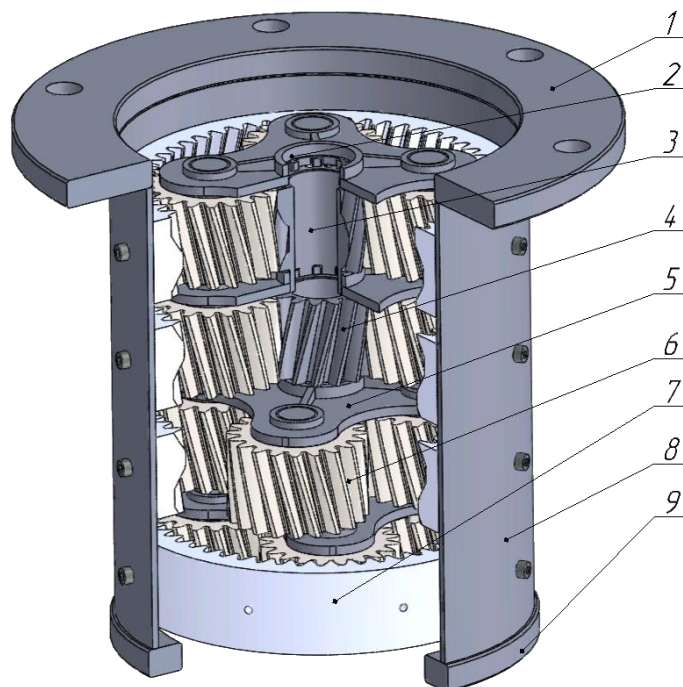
Компьютерная модель сборки планетарного редуктора (поступенчатый разрез): 1 – фланец для крепления к мачте, 2 – пазы зацепления с фланцем спирального диска трехкулачкового блока, 3 – сквозное отверстие, 4 – малая шестерня (солнце), 5 – водило, 6 – большая шестерня-планета (сателлит), 7 – эпицикл, 8 – корпус редуктора, 9 – фланцевое крепление для мотора.
